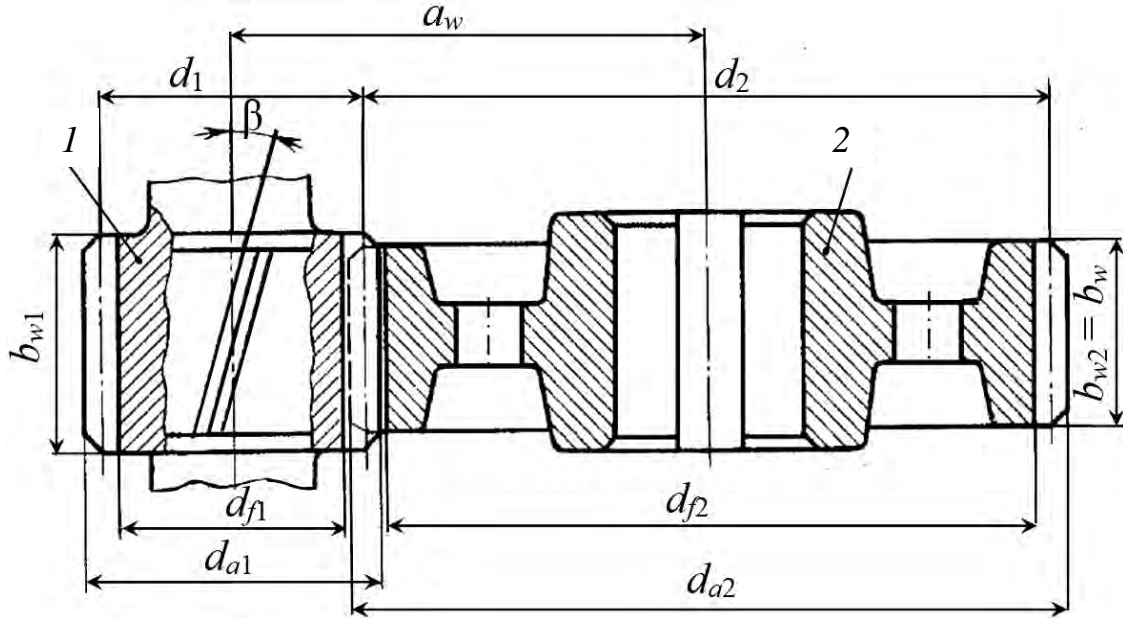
Геометрические параметры косозубой цилиндрической зубчатой передачи: 1 – шестерня; 2 – колесо
